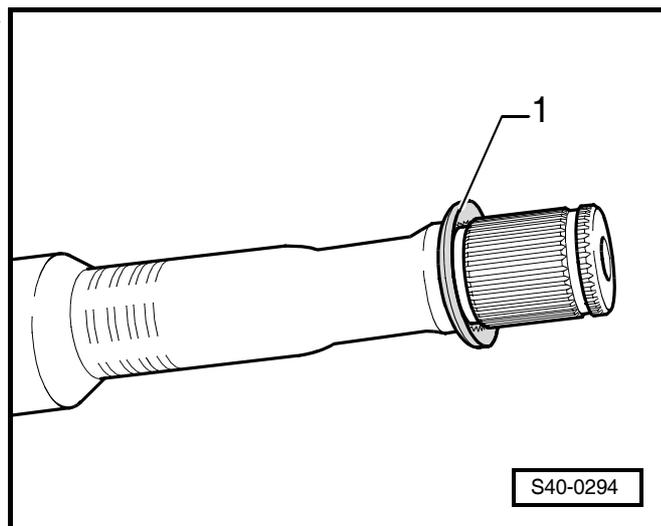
Положение для сборки тарельчатой пружины и упорное кольцо на наружном шарнире ►
